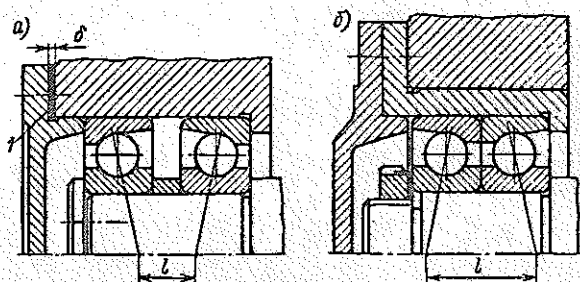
Конструкции фиксирующих опор с двумя радиально-упорными подшипниками
